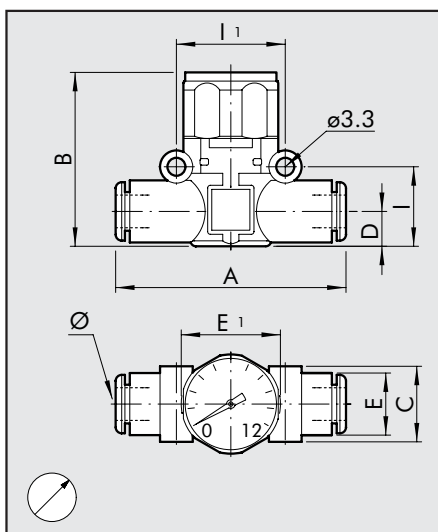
Abb. C: Wandbefestigung der MAN L mittels zweier Schrauben
